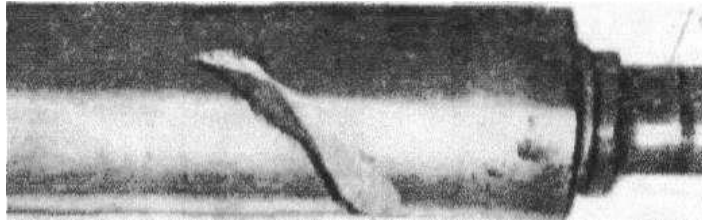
Викришування (сколювання) на бочці робочого валка діаметром бочки 500 мм із сталі 9Х2МФ: 1-бочка; 2- шийка
